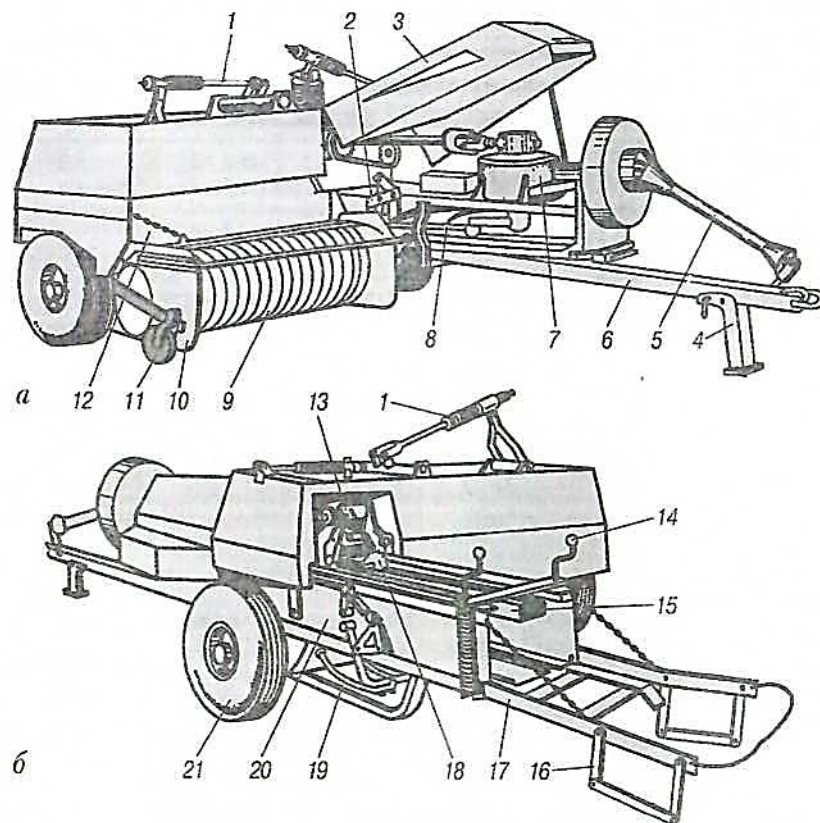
Прес-підбирач ПС-1,6: *а* – вид спереду; *б* – вид ззаду; 1 – механізм пакування; 2 – механізм підняття підбирача; 3 – капот; 4 – підставка; 5 – карданна передача; 6 – сниця; 7 – редуктор головної передачі; 8 – поршень із шатуном; 9 – підбирач; 10 – щиток; 11 – копіювальне колесо; 12 – приймальна камера; 13 – в’язальний апарат; 14 – регулятор щільності паки; 15 – брус регулятора щільності; 16 – рамка; 17 – лоток; 18 – мірильне колесо; 19 – голка; 20 – пресувальна камера; 21 – ходове колесо
